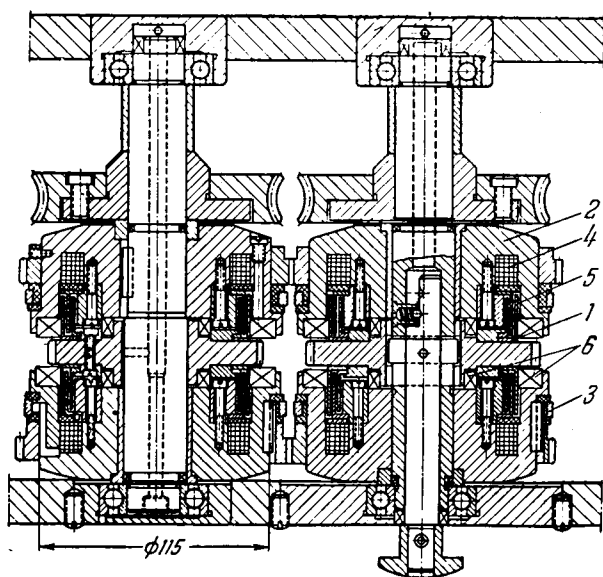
Порошковые муфты к токарно-винторезному станку.
